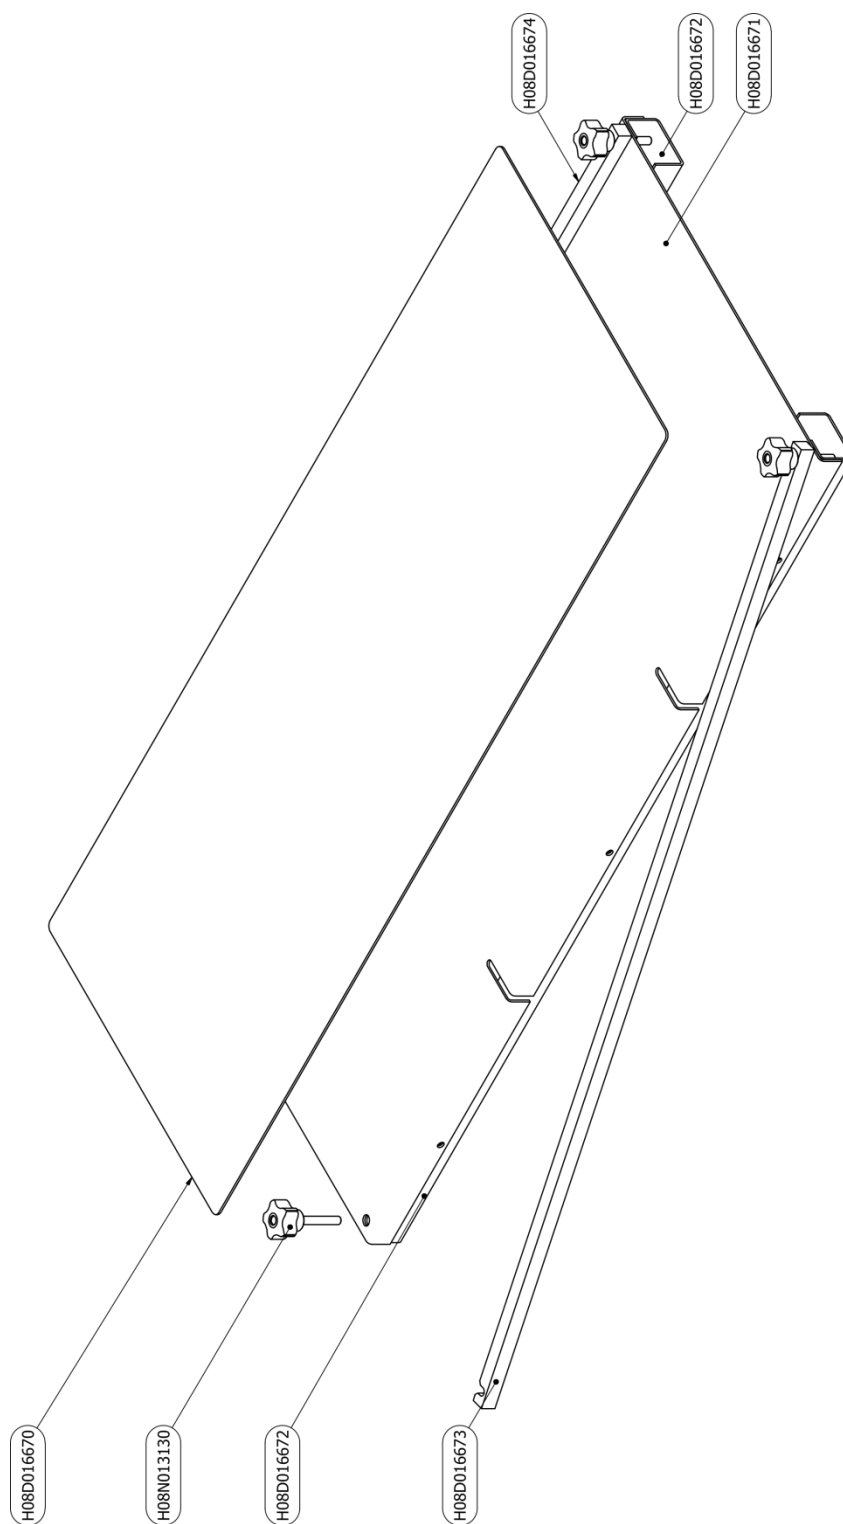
H08D016669 Plaque de soudage PML-600
